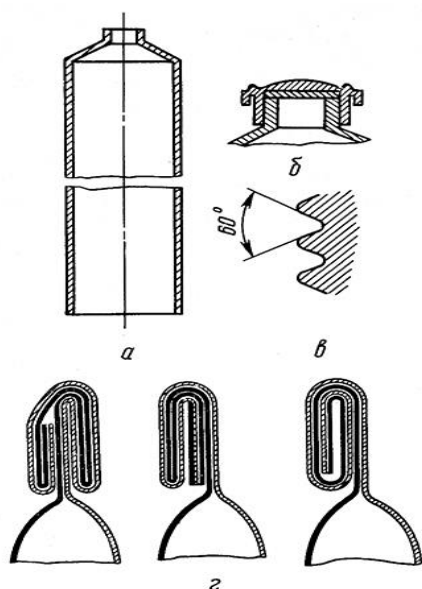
Алюминиевая туба с колпачком и типы швов: а - общий вид тубы; б - носик тубы с бутонем и прокладкой; в - профиль резьбы; г - типы
